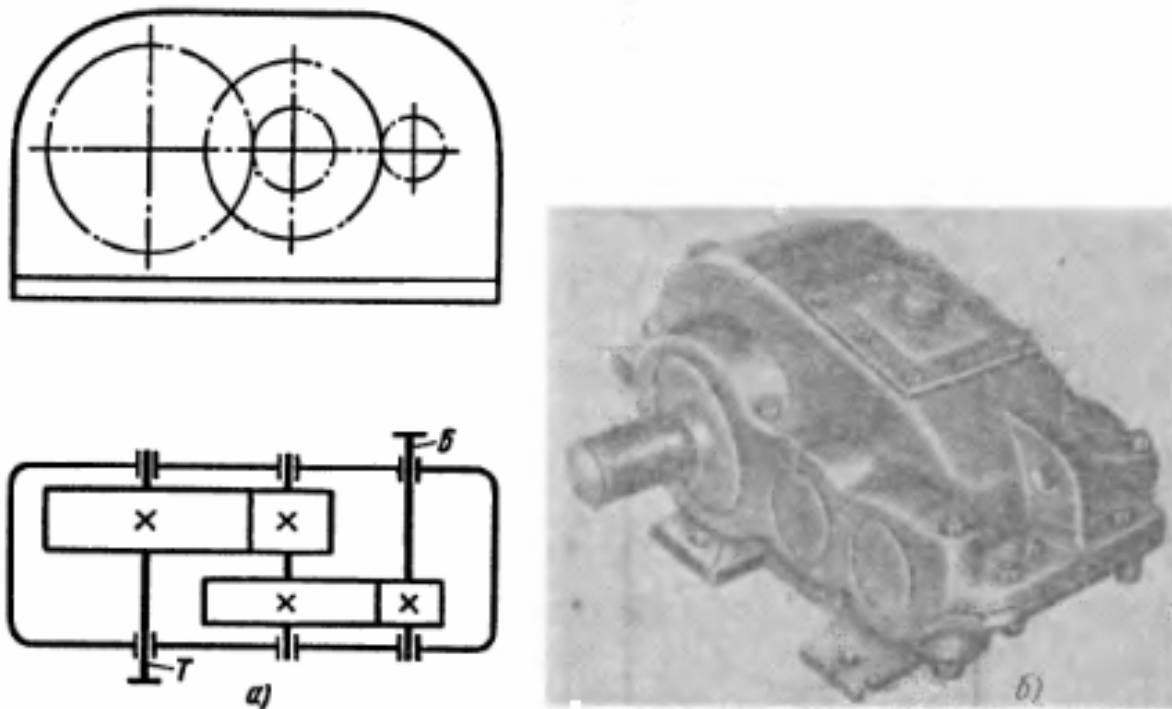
Цилиндрический двухступенчатый редуктор с развернутой схемой:
